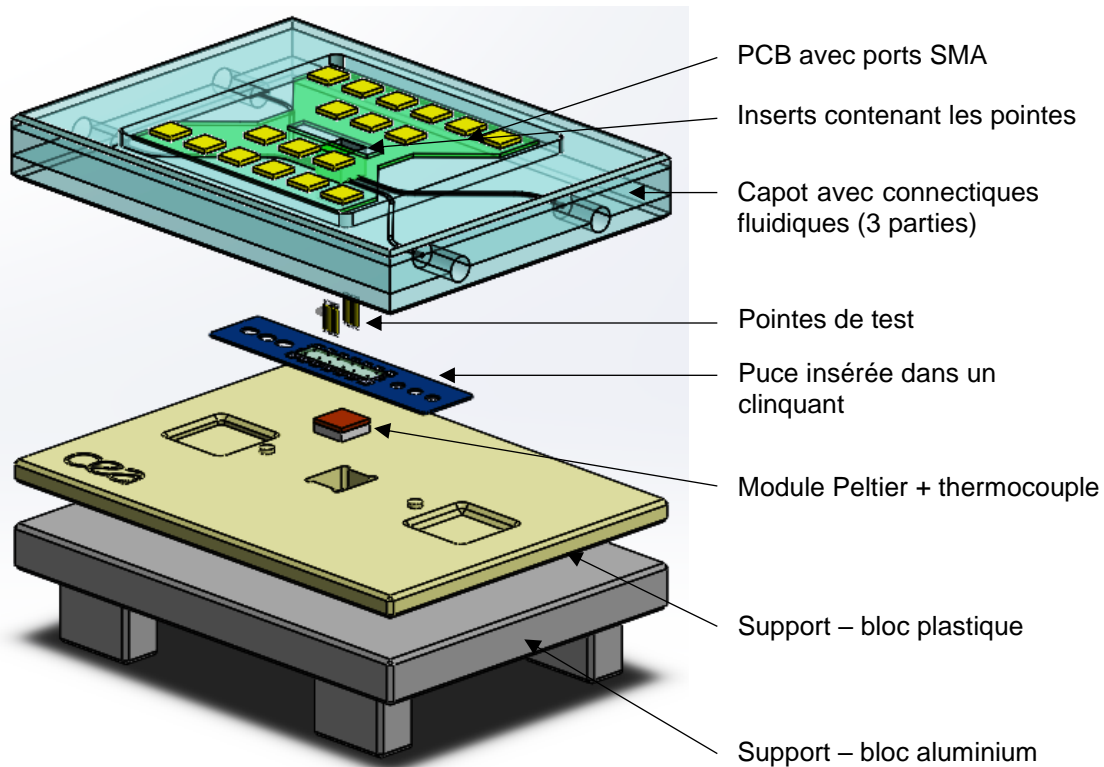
Vue éclatée de la plateforme comportant le bloc fluidique en face avant.
